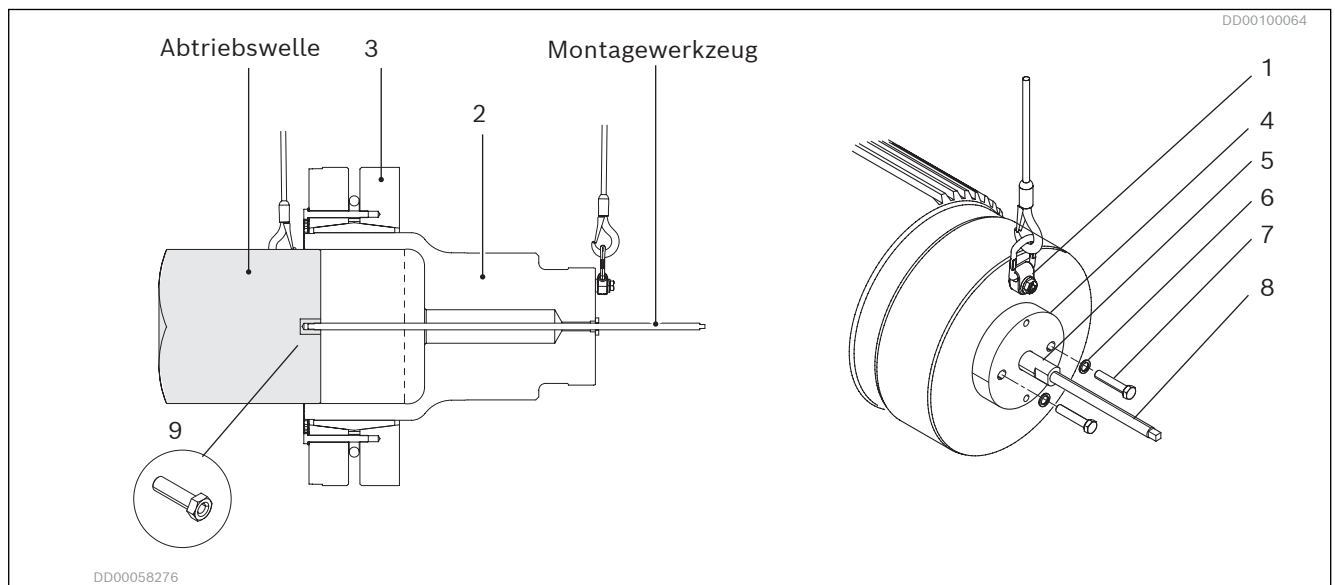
Montage von Kupplungsmotor mit Montagewerkzeug
